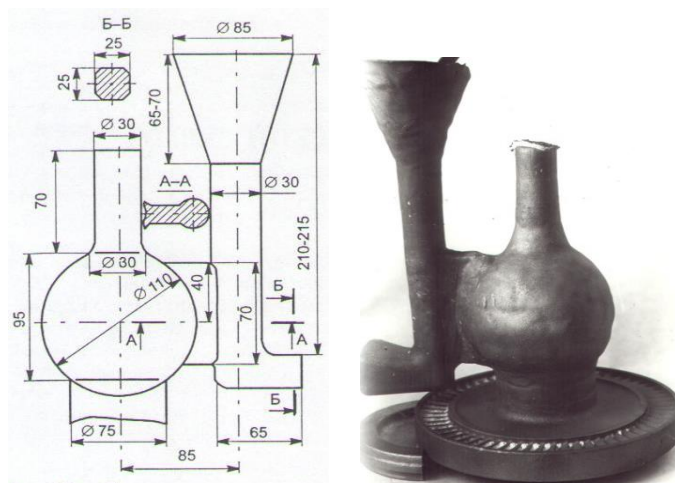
Чертеж разработанной ЛПС и отливка диска
